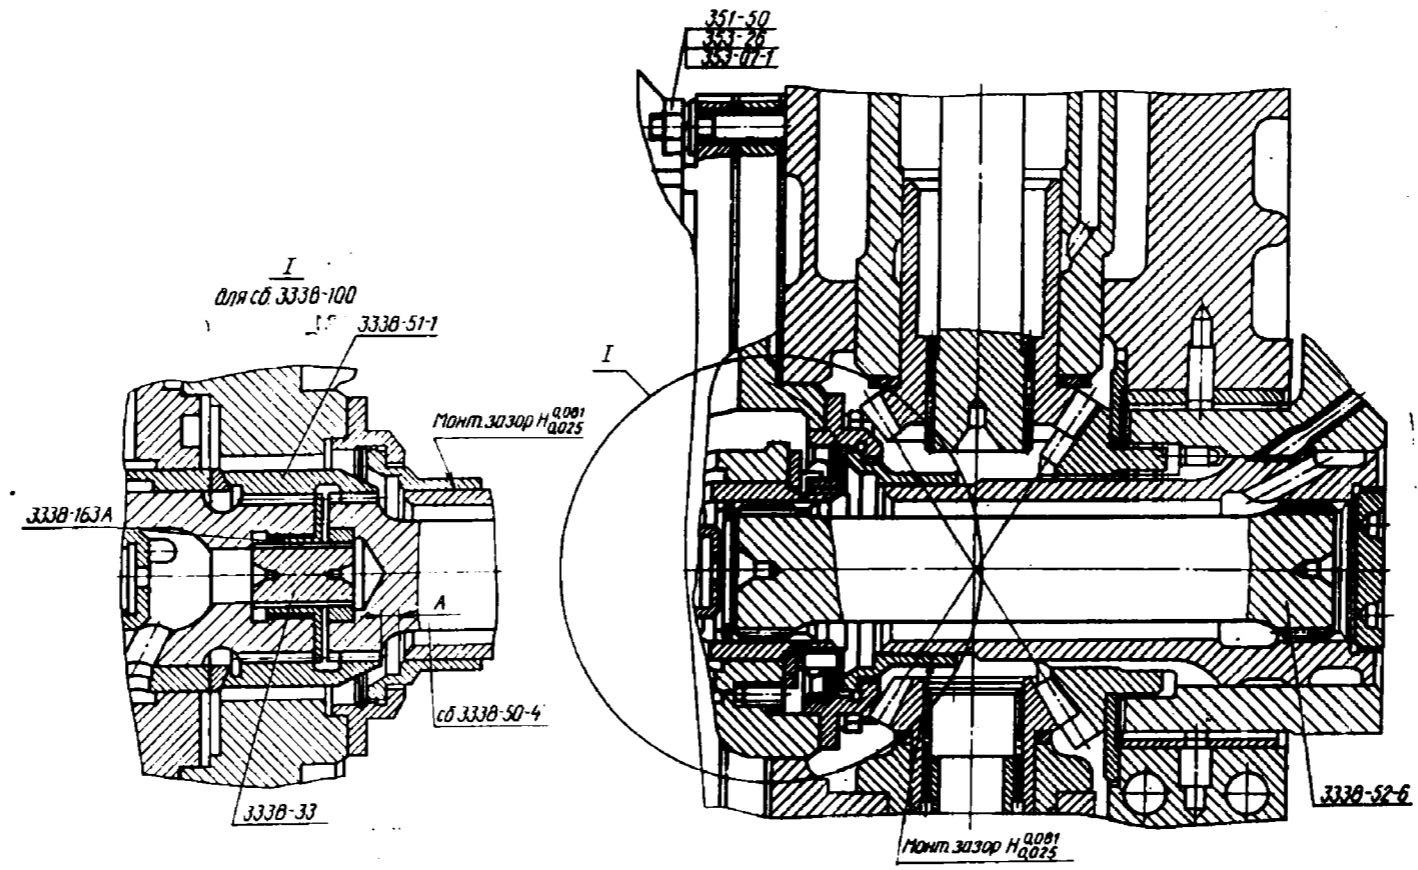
Установка нагнетателя сб.3338-00-1 и сб.3338-100:
